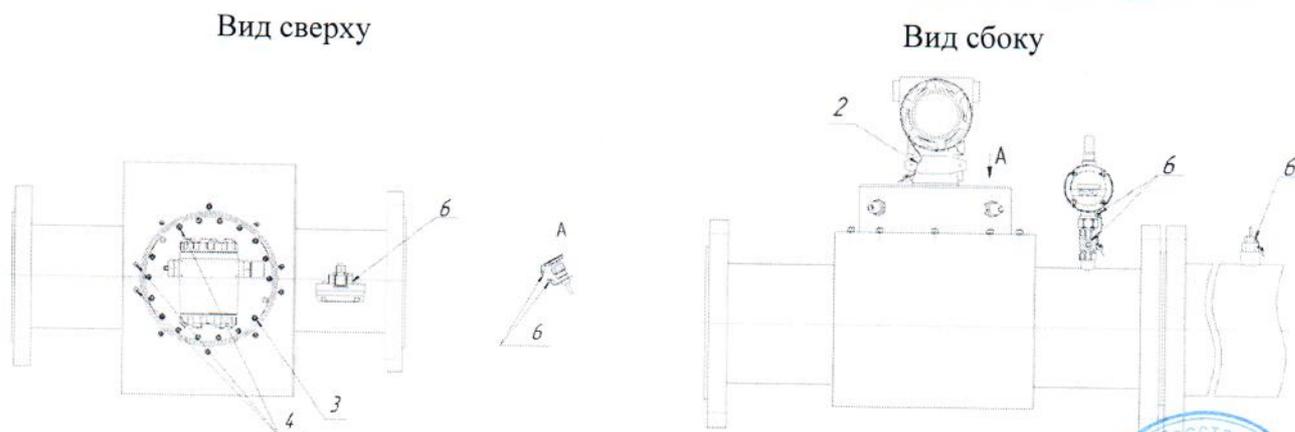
Корпус круглого сечения с защитным кожухом
